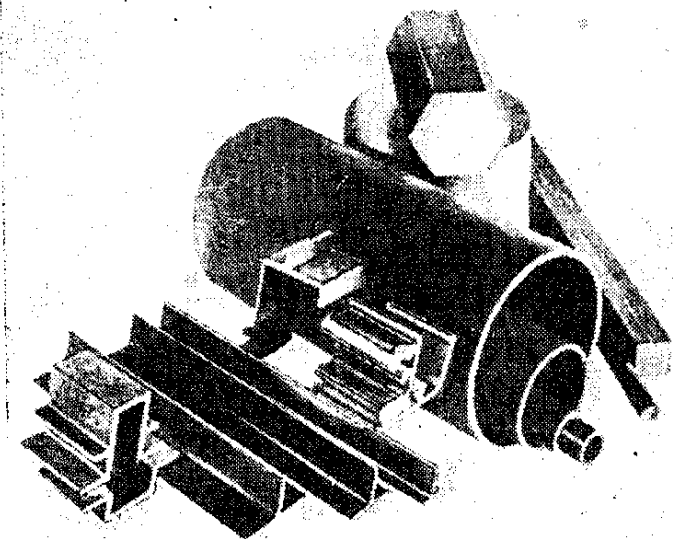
Прессованные трубы, профили и прутки из магниевых сплавов
